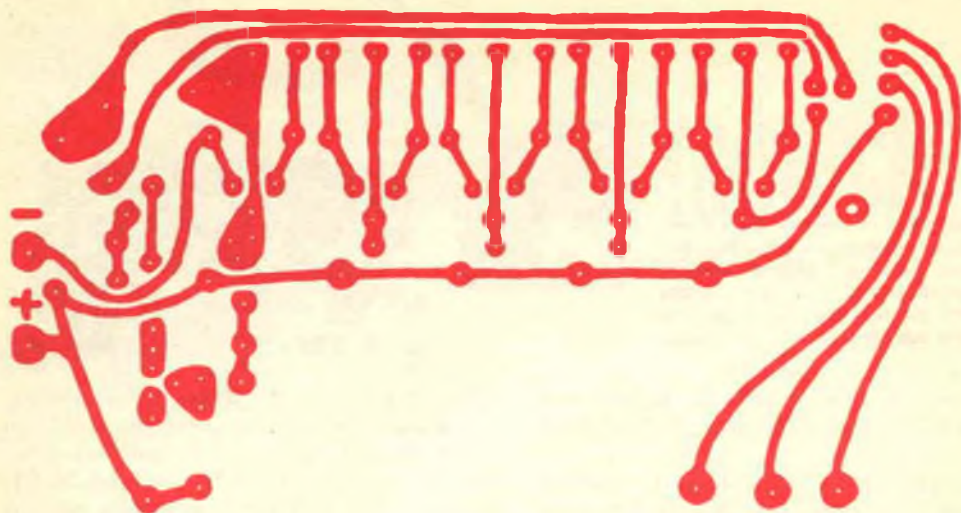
Circuito stampato e disposizione dei componenti della serratura elettronica.
